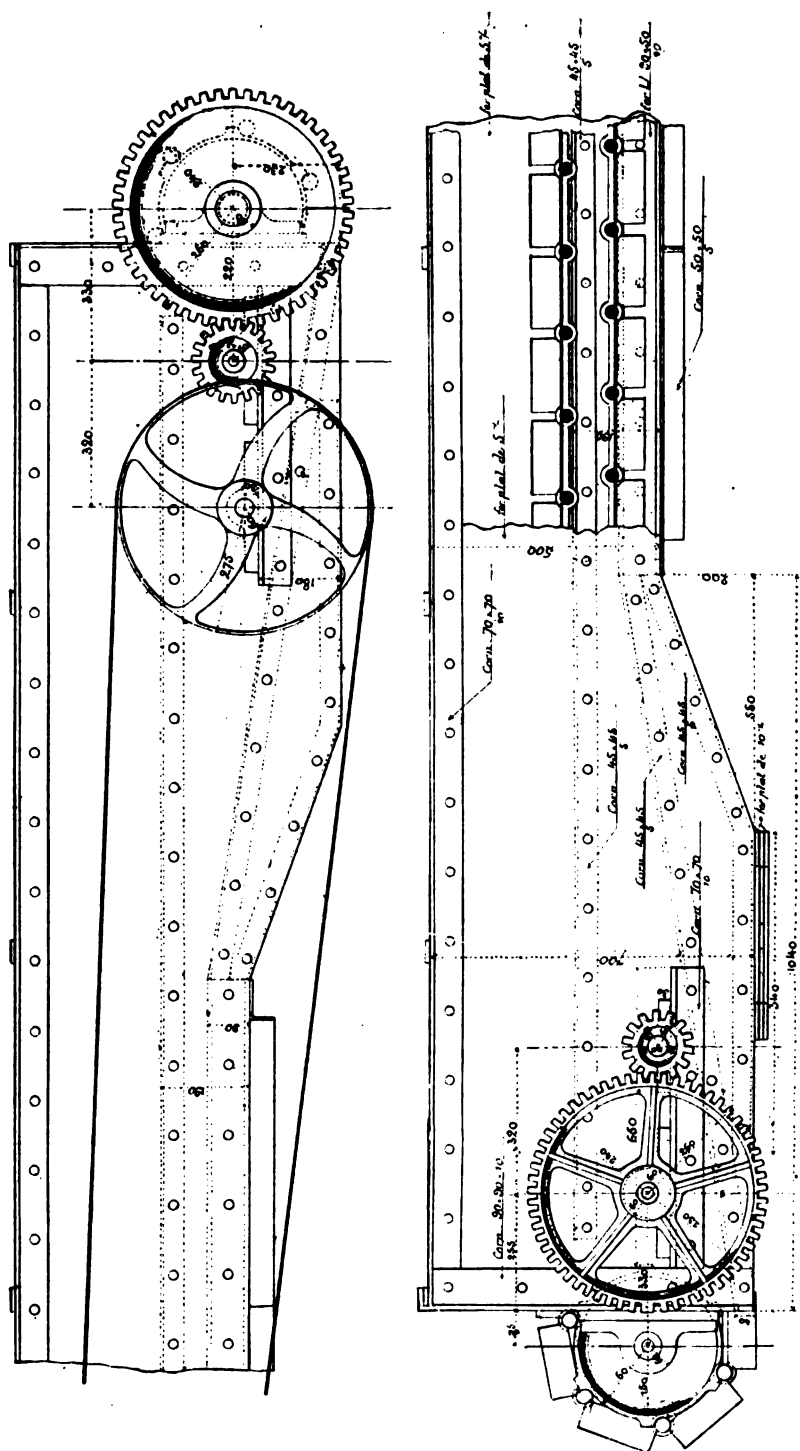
Extrémité arrière du transporteur. Élévation des deux faces latérales.
